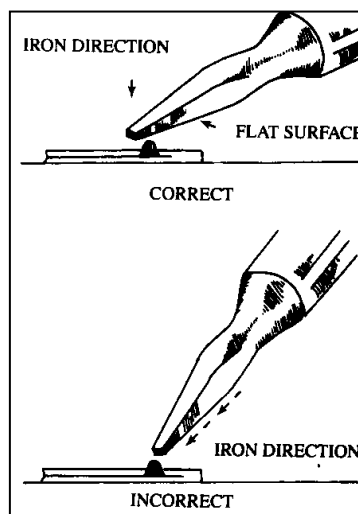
Maneras para aplicar la soldadura.
